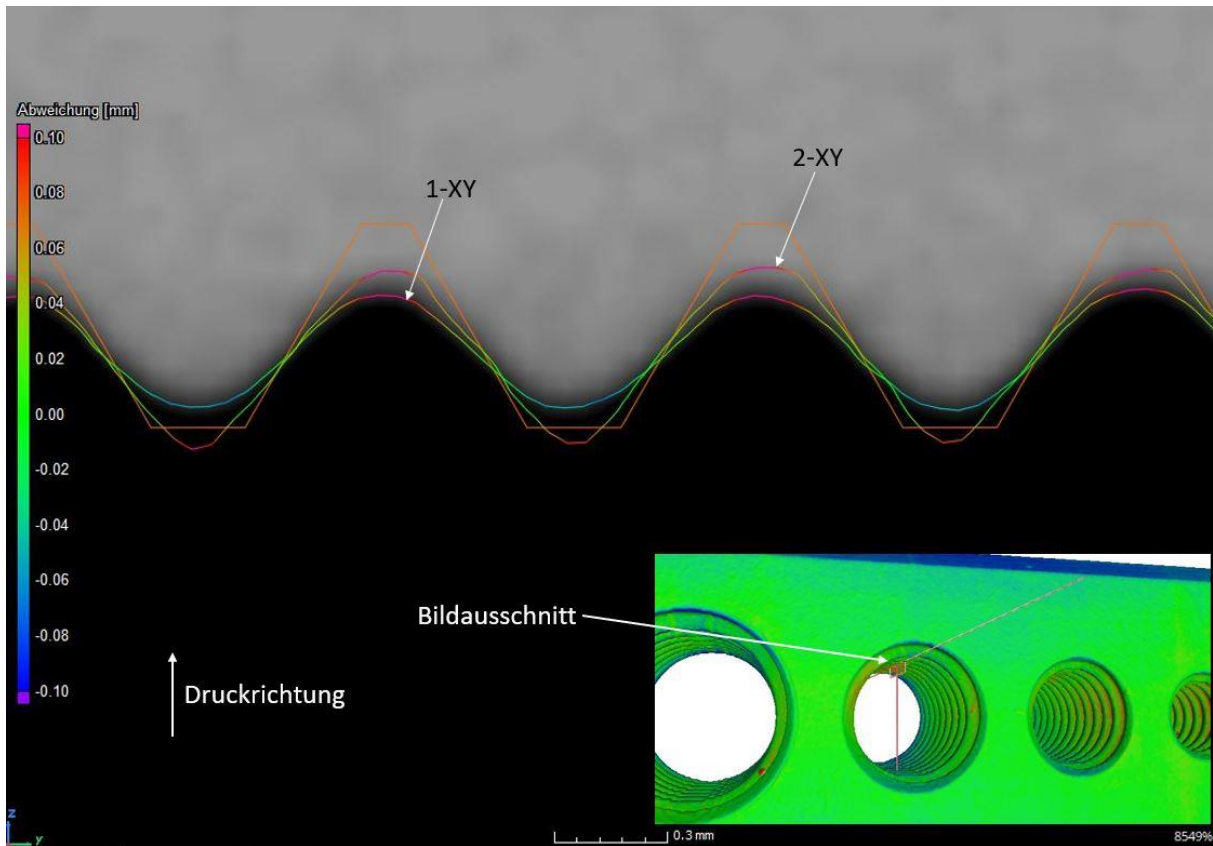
Detail Ansicht M6 Proben 1-XY und 2-XY. Hängende Gewindeflanke
